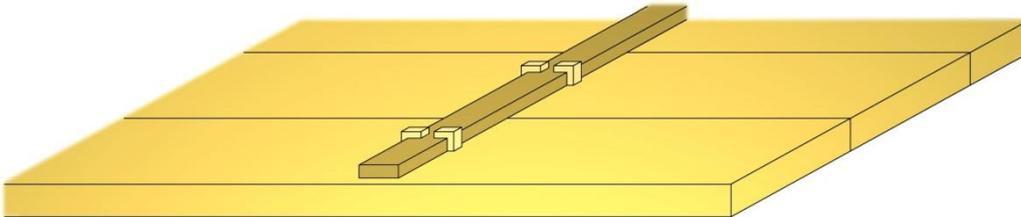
Travesaño con forma rectangular sujeto por abrazaderas encoladas.
